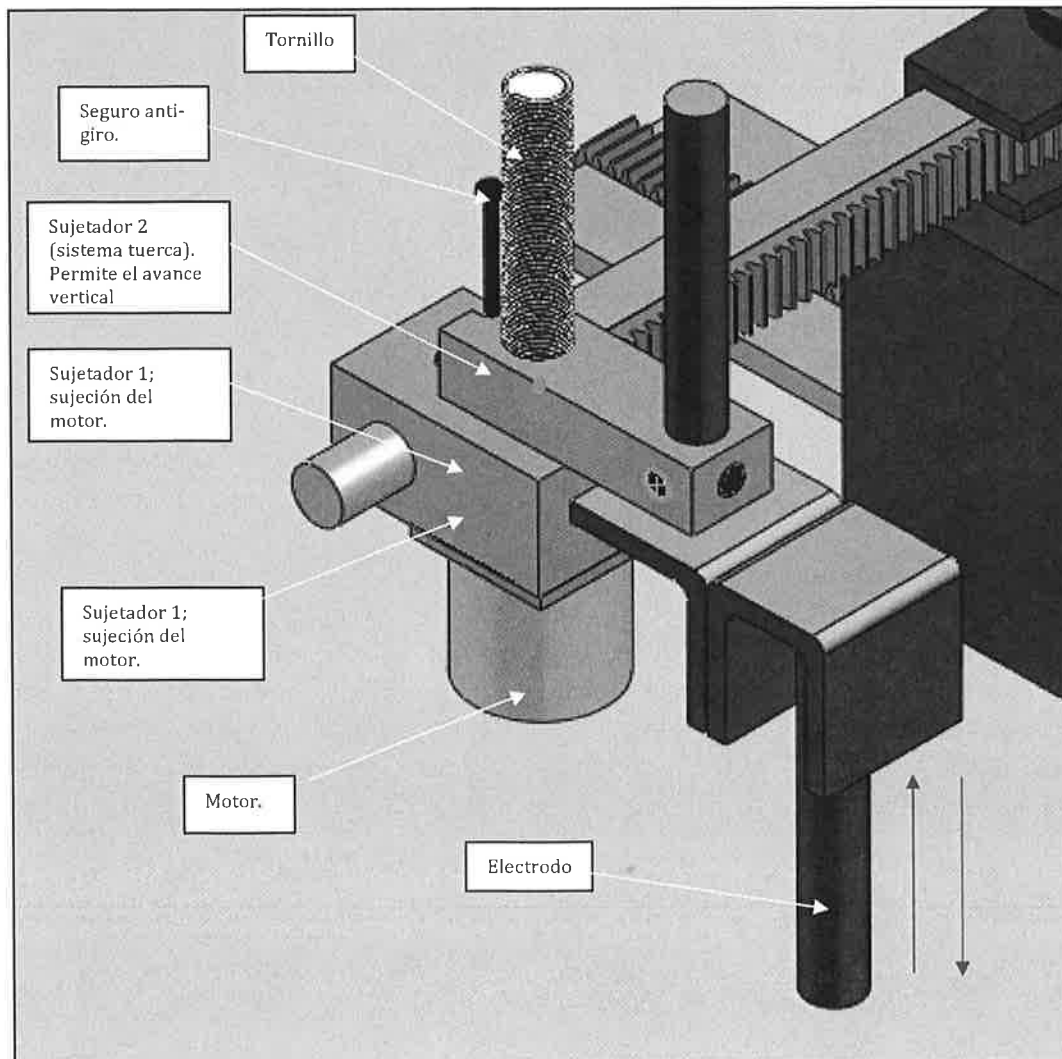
Ensamble final dispositivo tornillo-tuerca en eje Z.
